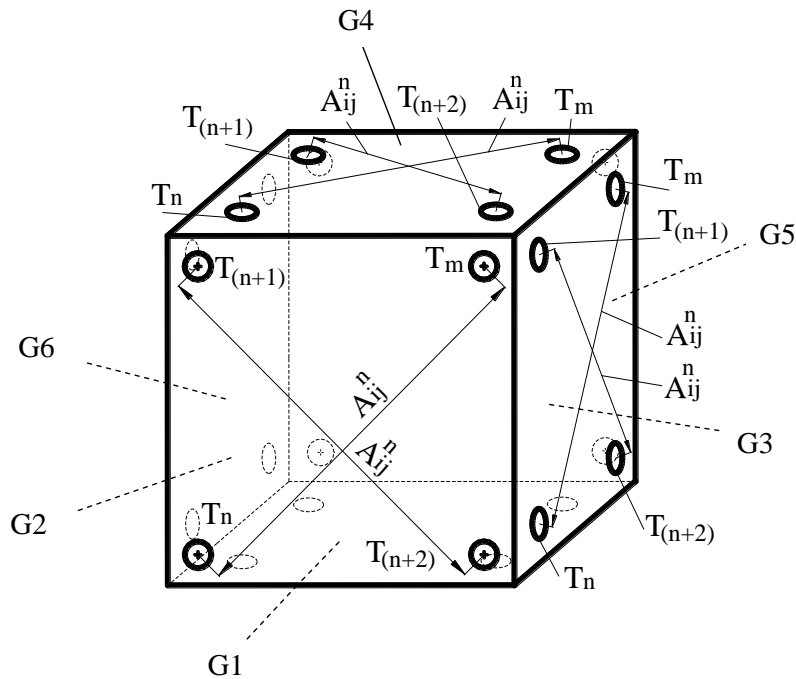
Модель носителя с базирующими отверстиями, расположенными на боковых гранях G призматического корпуса
